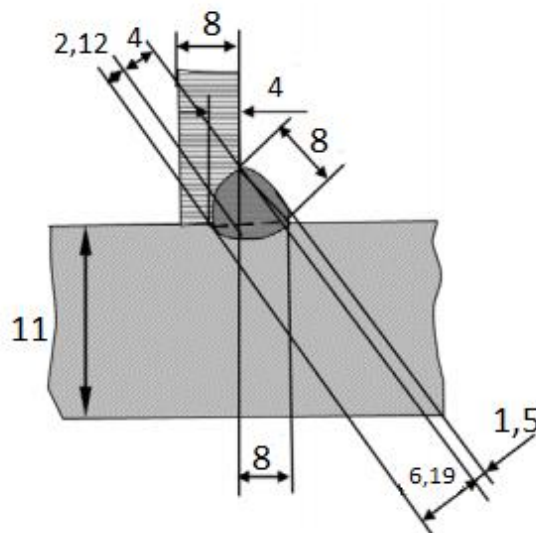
Геометрические размеры сварного шва, мм
